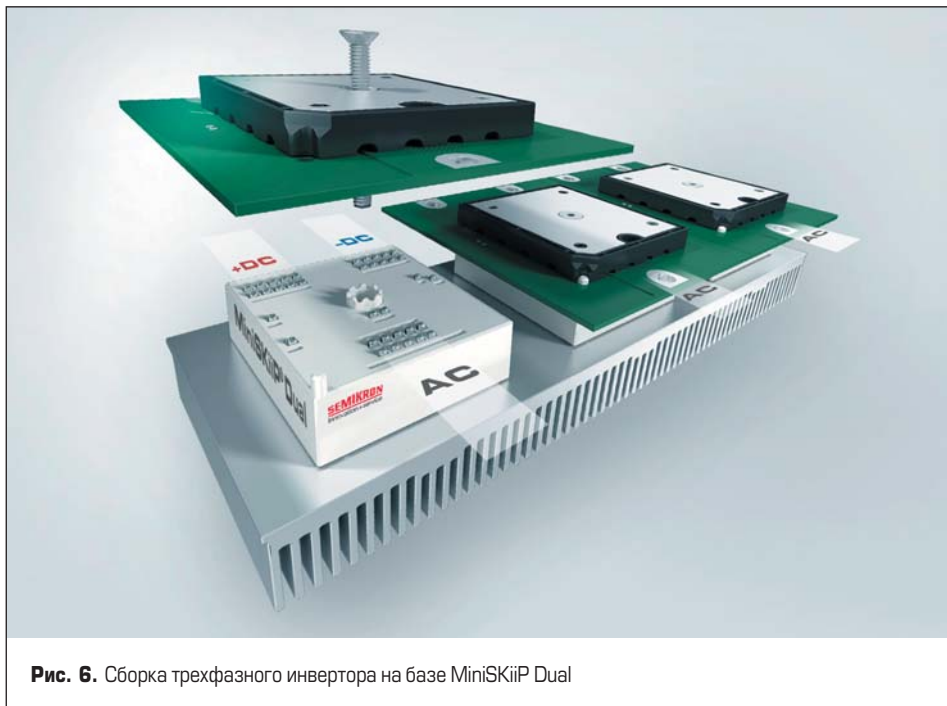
Сборка трехфазного инвертора на базе MiniSKiiP Dual
